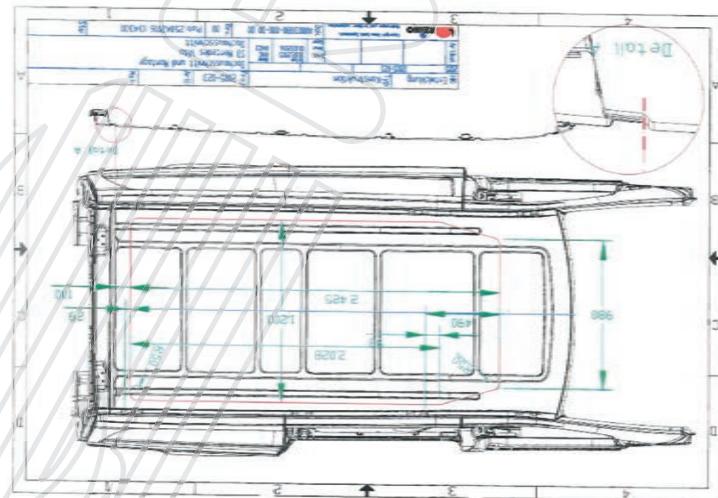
Zeichnung Dachauschnitt 3
